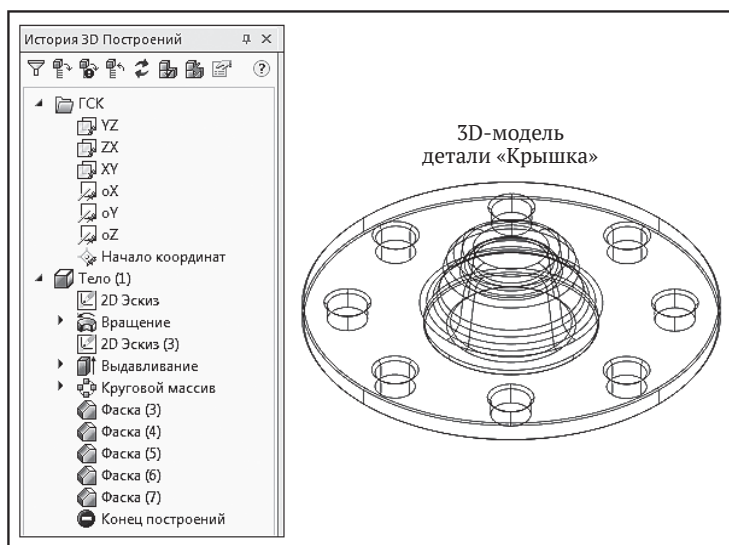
Пример 3D-модели детали «Крышка» и истории ее построения (визуальный стиль Каркас)
